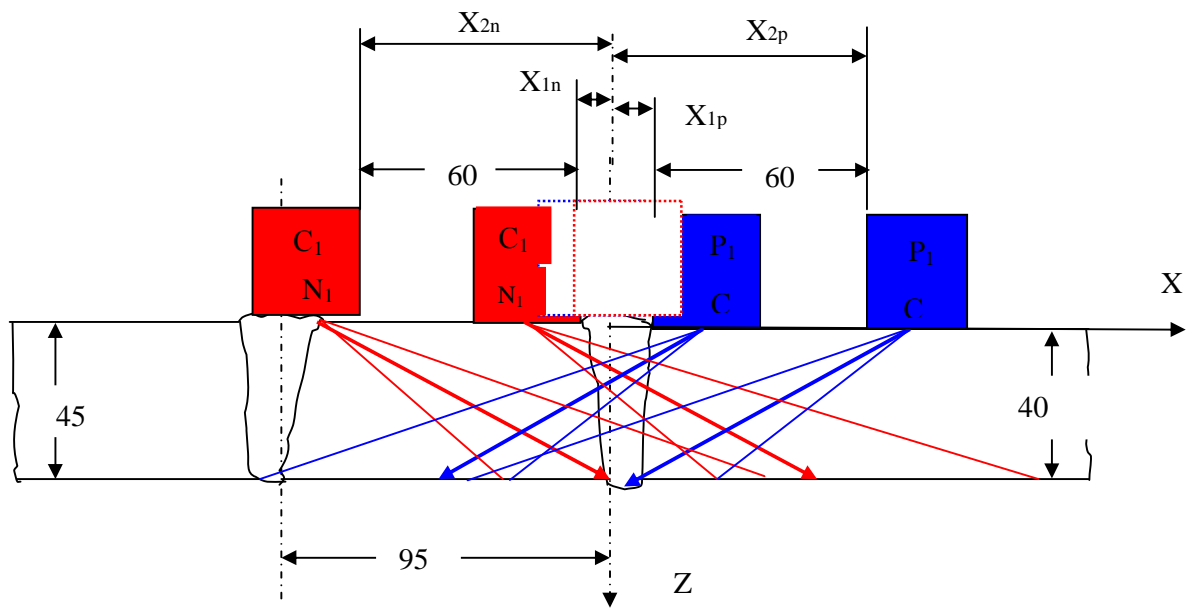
Схема контроля сварных соединений патрубков вакуумной камеры ИТЭР.
